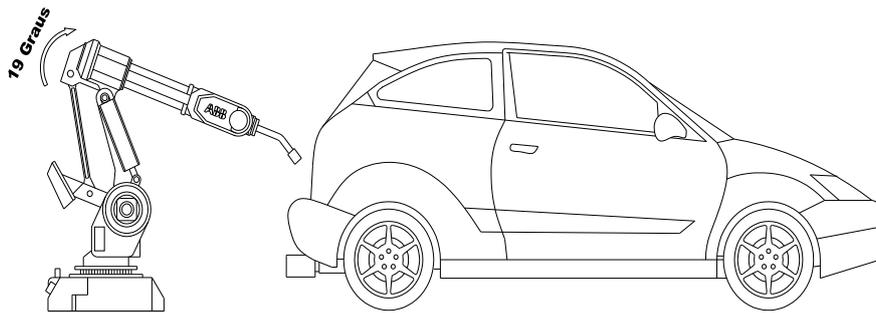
Figura-exercício 16.2 Principais movimentos do robô no processo de soldagem.
